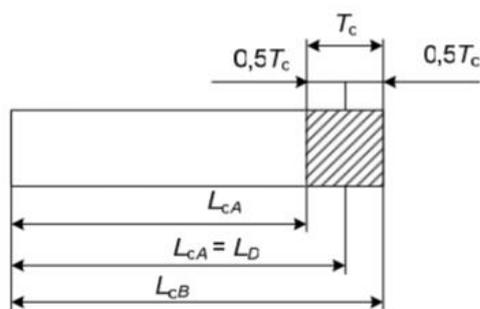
Взаимосвязь между номинальным размером до необрабатываемой поверхности детали, номинальным, предельными размерами и допуском отливки [3, с. 27].
